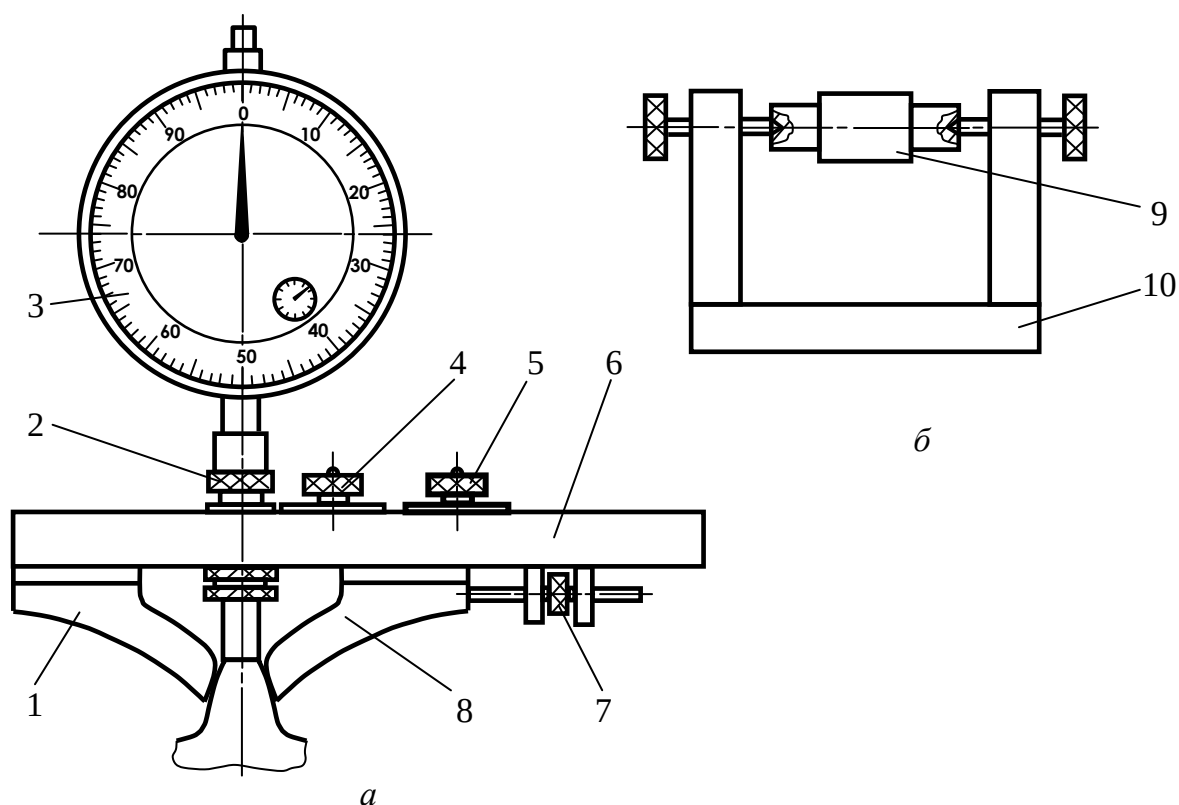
Измерение смещения исходного контура ЗК с помощью тангенциального зубомера: а – тангенциальный зубомер; б – ролик для настройки прибора; 1, 8 – измерительные губки; 2 – гайка; 3 – индикатор часового типа; 4, 5 – винт; 6 – корпус; 7 – микровинт; 9 – цилиндрический ролик; 10 – стойка
